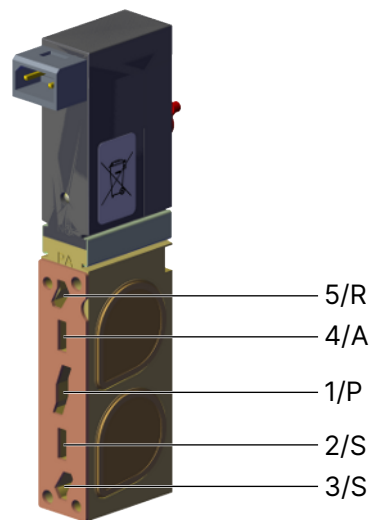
Anschlussbelegung 5/2-Wege-Ventil
